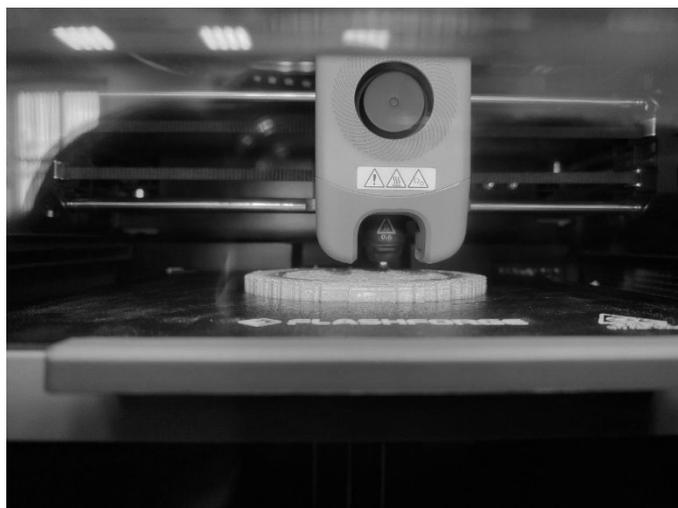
Деталь, изготовленная из TPU-95A пластика
